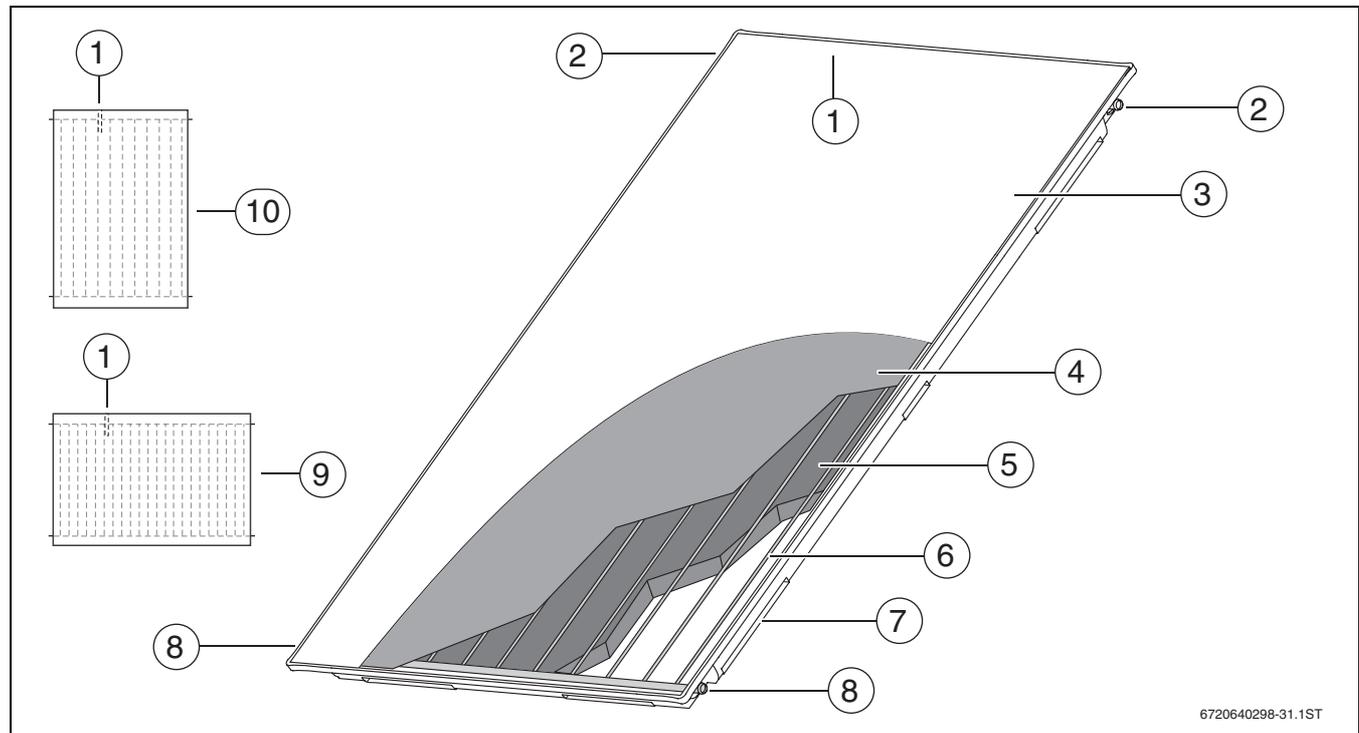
Kollektortyp senkrecht in geschnittener Darstellung
